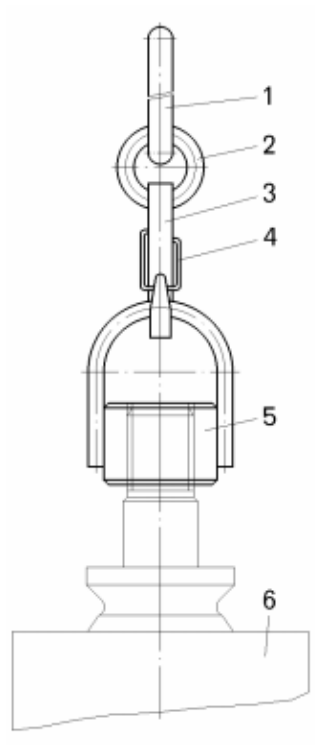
Чалочное приспособление для транспортировки цилиндра подвески:
